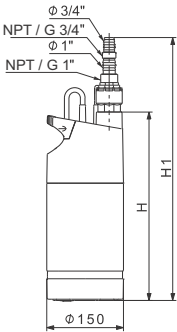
SB-Pumpe. Gleiche Abmessungen mit eingebautem und mit schwimmendem Zulaufsieb.
